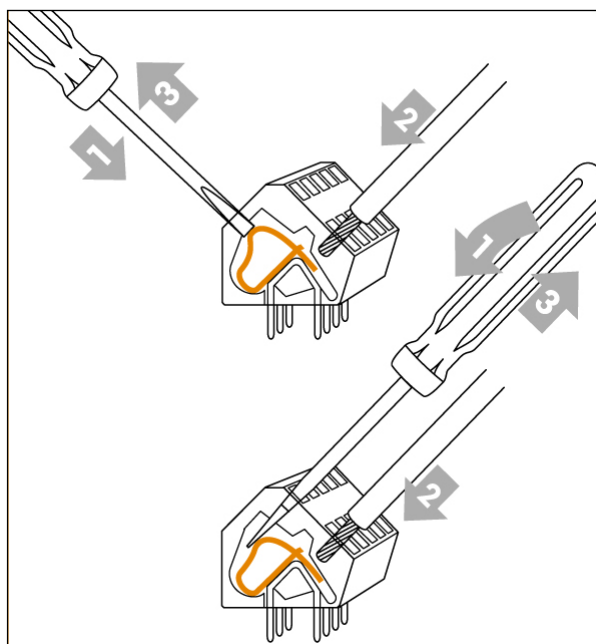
Anschluss technik: WAGO CAGE CLAMP®
